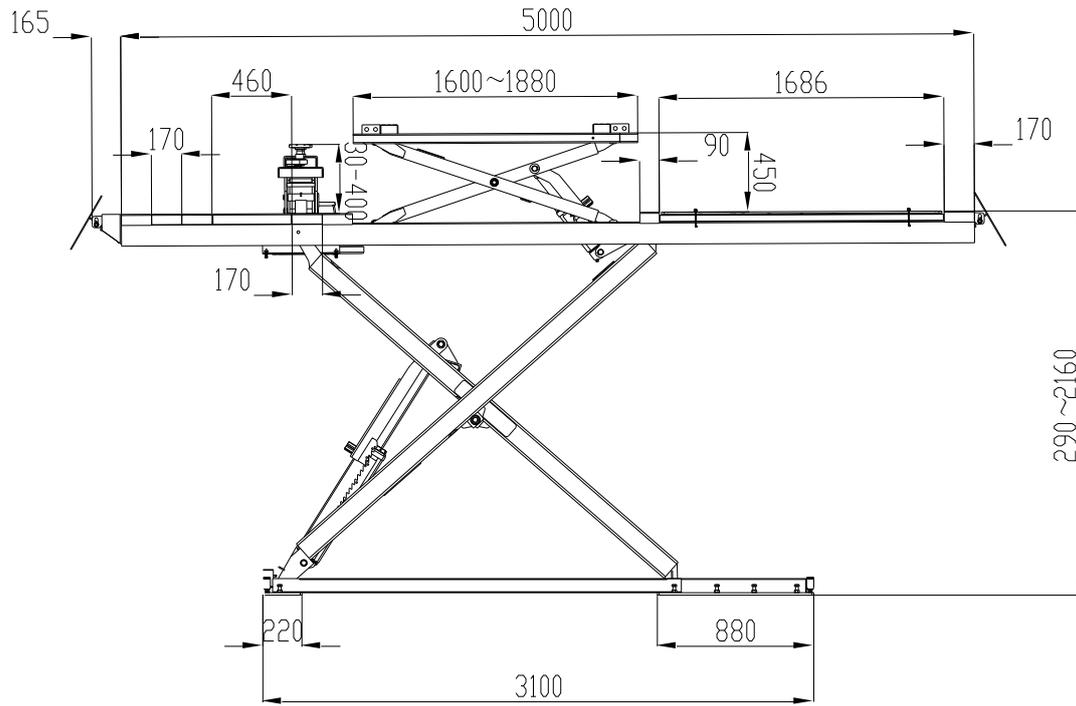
(5) – Grundriss für Unterflurmontage RP-8250
